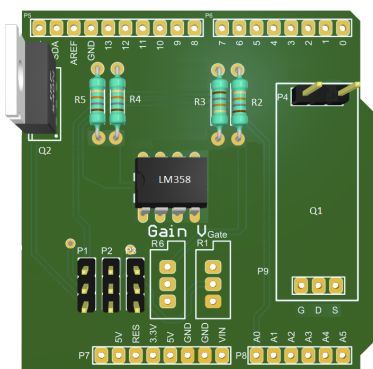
Ilustração da placa de circuito impresso do circuito condicionador do sinal de saída do EGFET.
